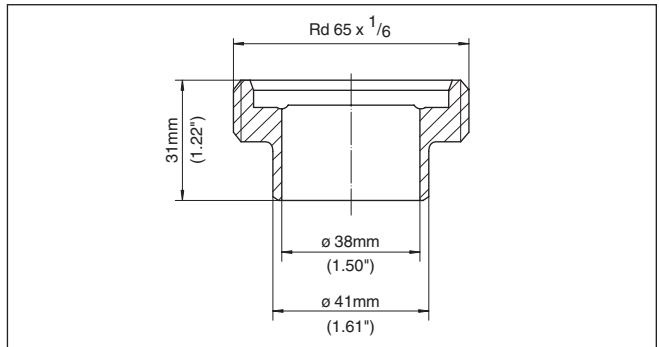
Maße Einschweißstutzen Rohrverschraubung DN 40 (DIN 11864-1)
